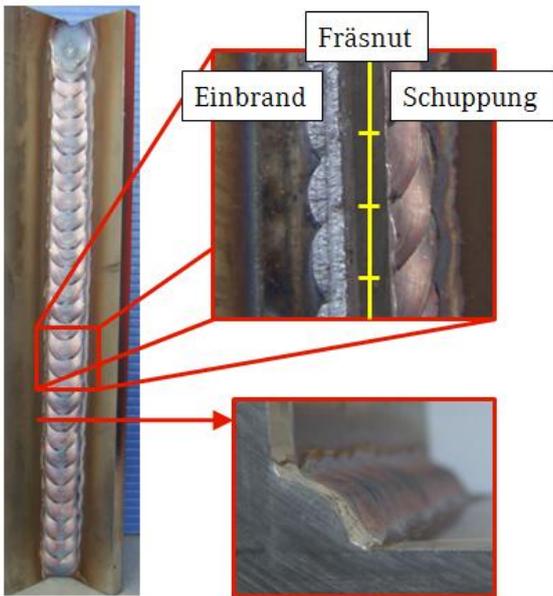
SpeedUp CrNi-Stahl 1.4301 t=4mm, Draht 1mm 1.4316 (ER308) 4.7m/min, 98%Ar+2%CO₂, 104A, 15V, 1.8kW, Schweißgeschwindigkeit 20cm/min, 5.4kJ/cm, handgeschweißt.
